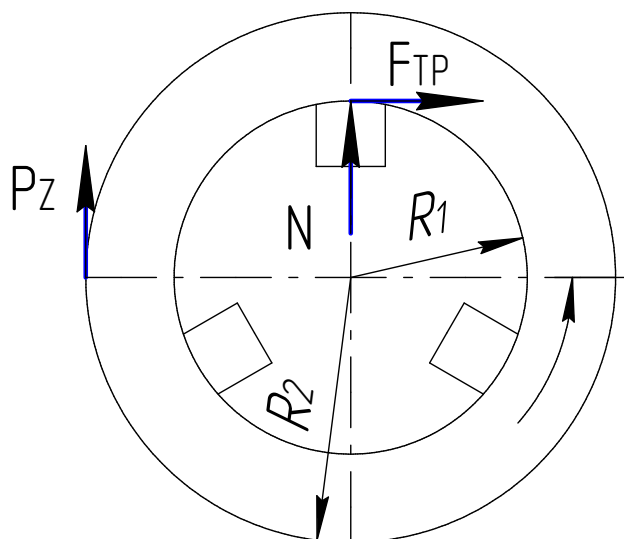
Схема сил, що діють на заготовку в процесі обробки.
